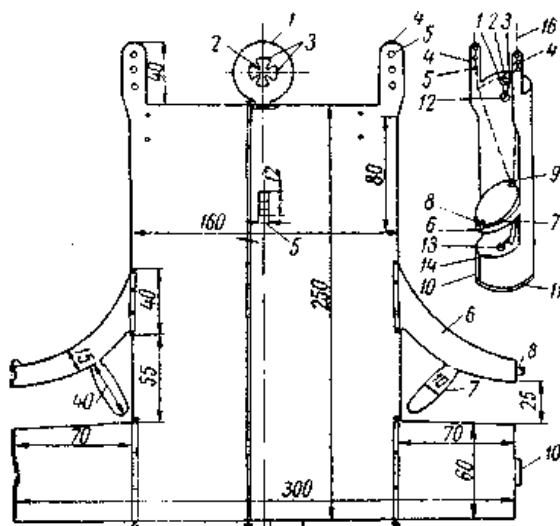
Развертка заготовки корпуса бурскопической приставки
